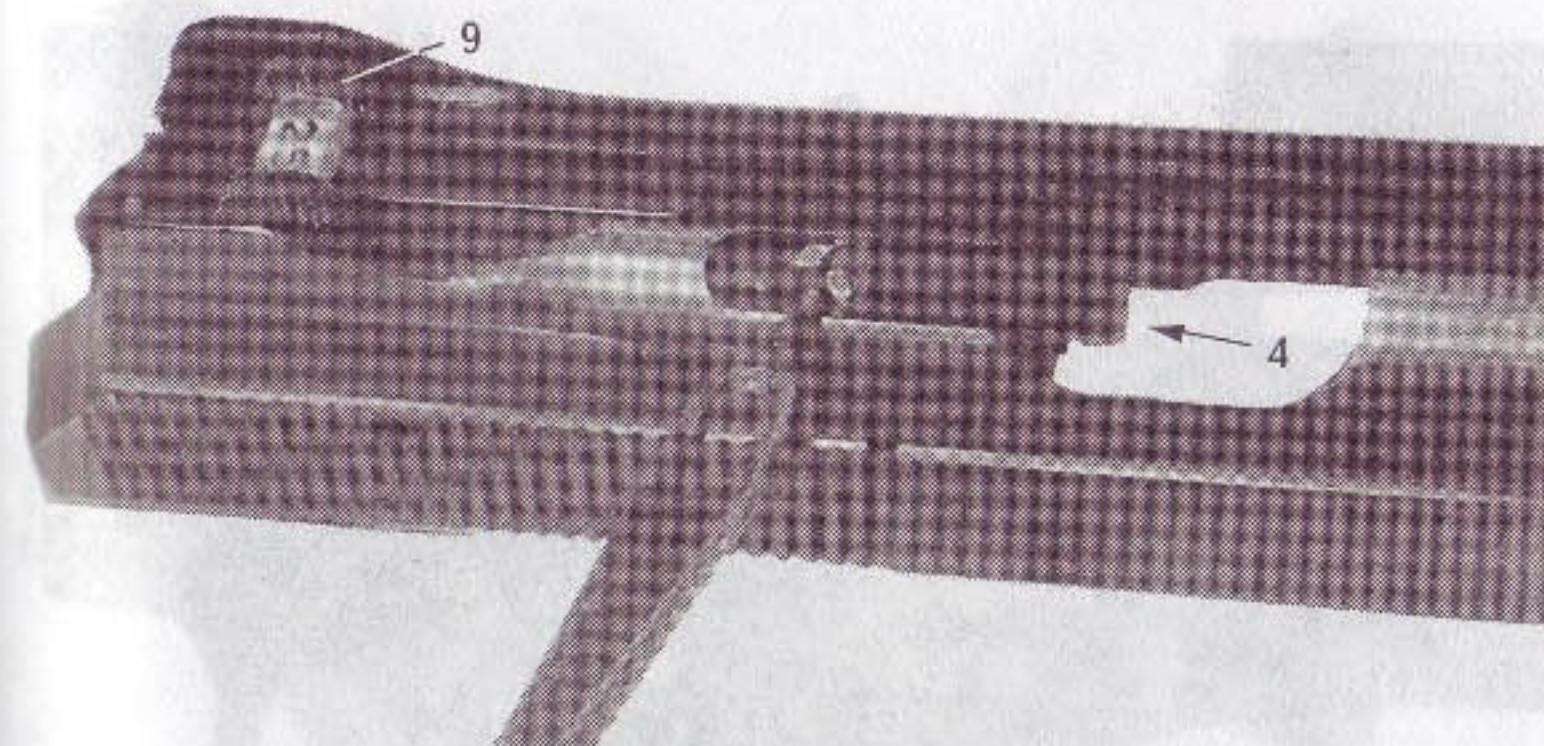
Полная разборка (разборка затвора): поднять любым острым концом заднюю часть выбрасывателя (4) и отделить его (9 — установочный прицельный барабанчик)
